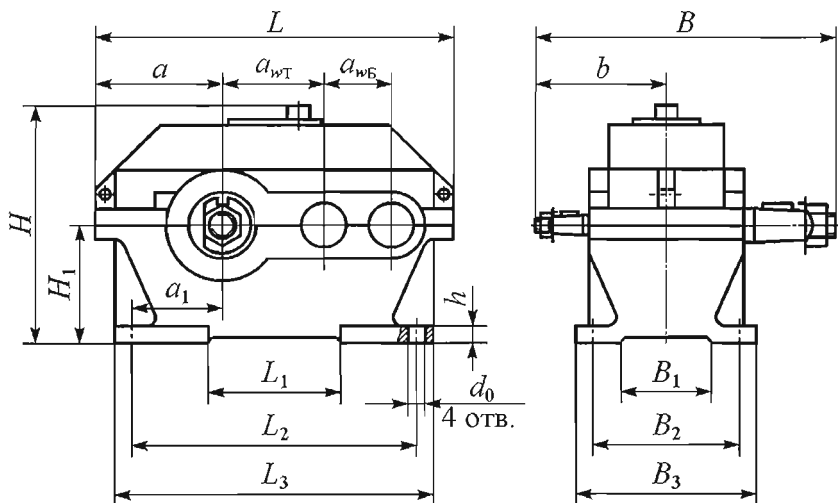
Габаритные, установочные и присоединительные размеры редуктора
